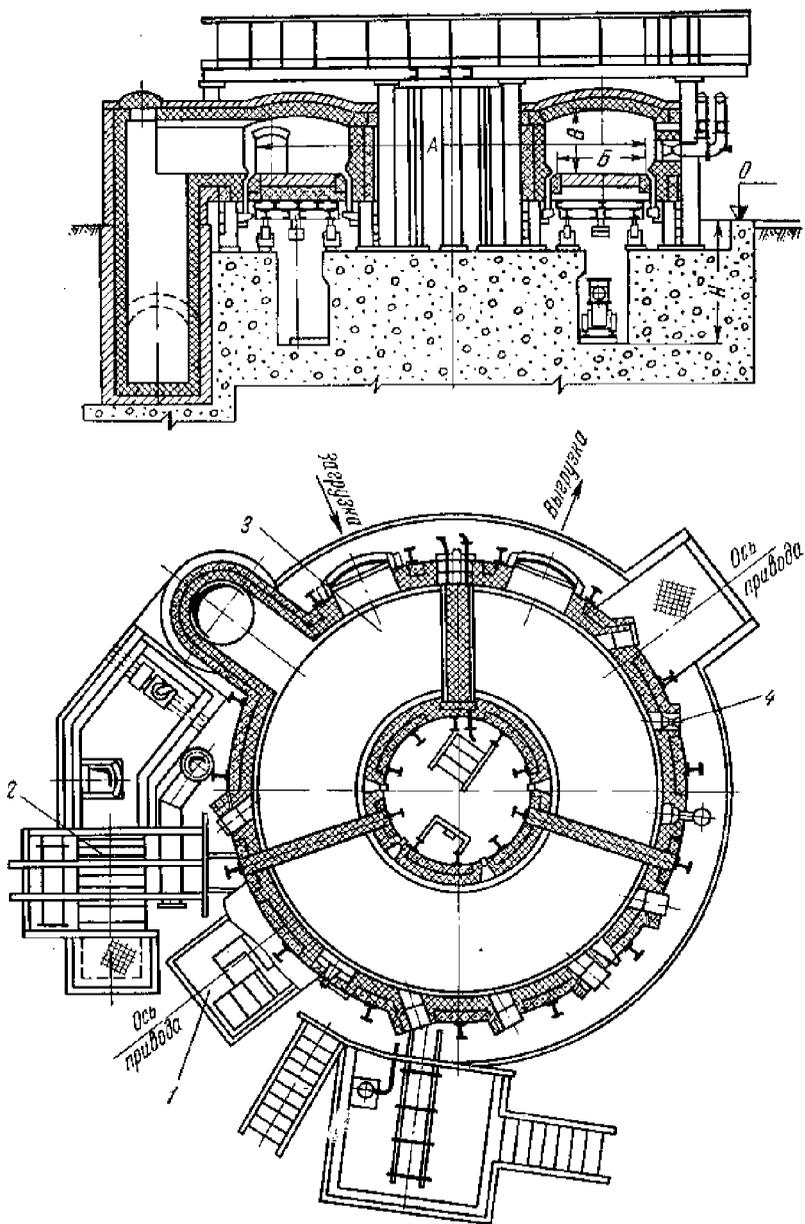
Нагревательные печи с вращающимся кольцевым подом НЛЮК: 1 – привод механизма вращения пода; 2 – рекуператор; 3 – вращающийся под; 4 – горелка
